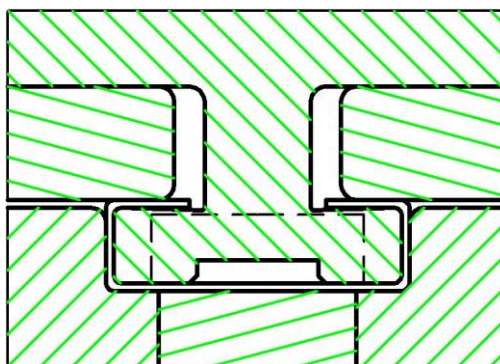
Гибка заготовки до окончательного изделия
